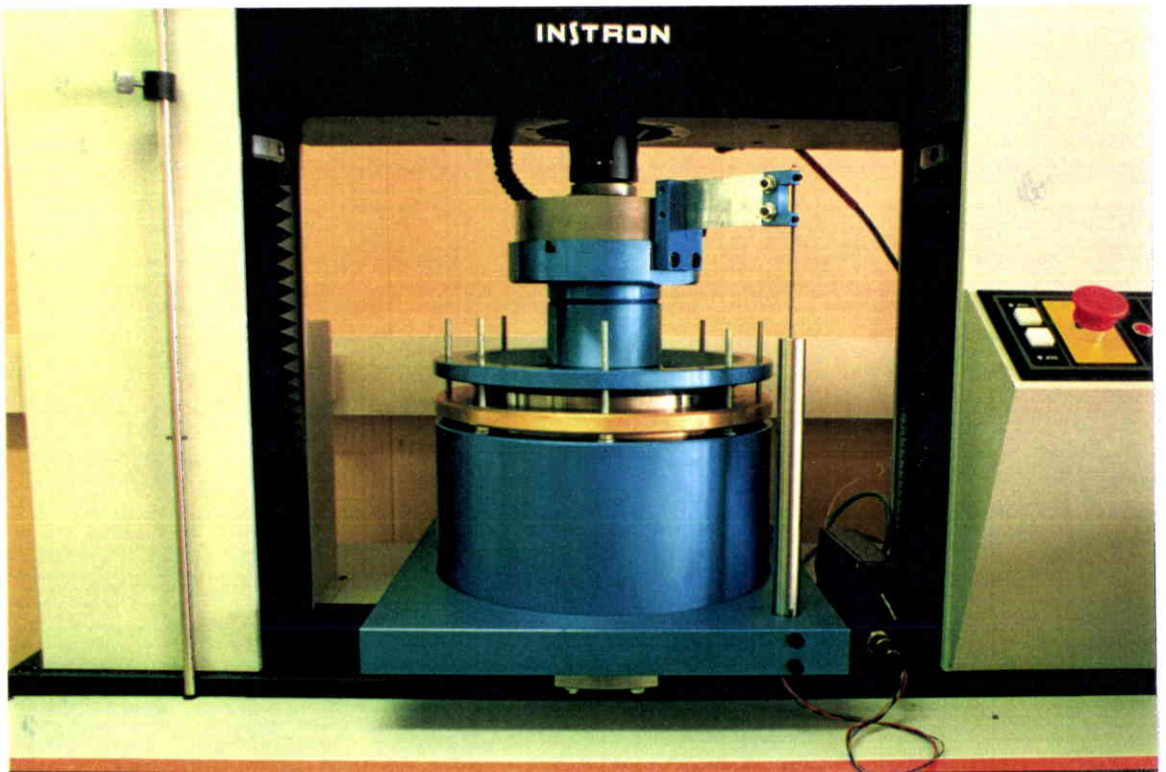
Vue de la maquette de forgeage des pignons en place sous la machine d'essai pilotée
